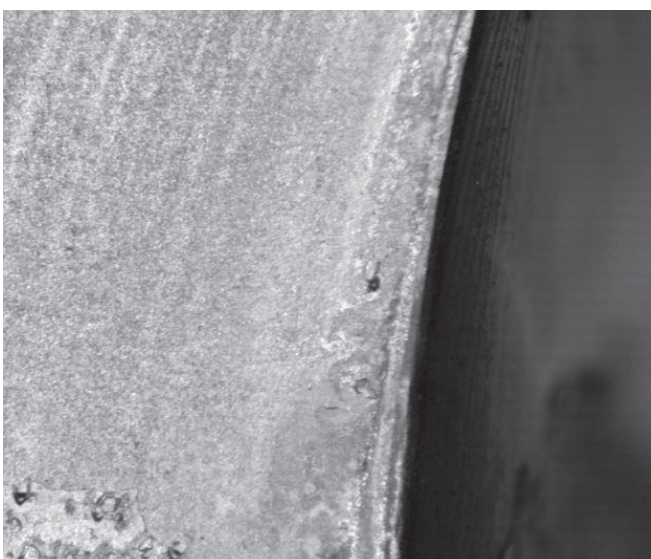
Przyklejona zalewka żuźlowa oraz zagłębienia w dolnej połowie elementu P2
